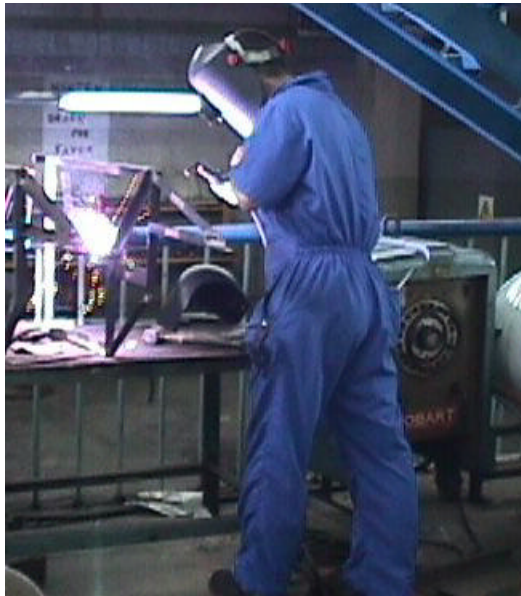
Máquina para soldadura eléctrica al arco (SMAW)”, modelo Progress, marca Bellyott, N° 2P, Londres, Inglaterra.
